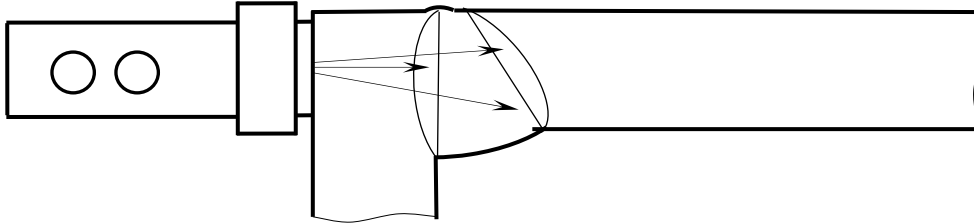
Схема контроля угловых сварных соединений прямым раздельно-совмещенным пьезоэлектрическим преобразователем
